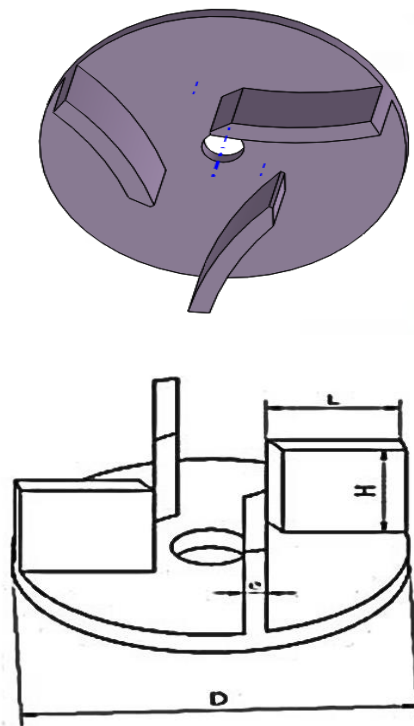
24.-Dimensiones geométricas de la turbina [21].
